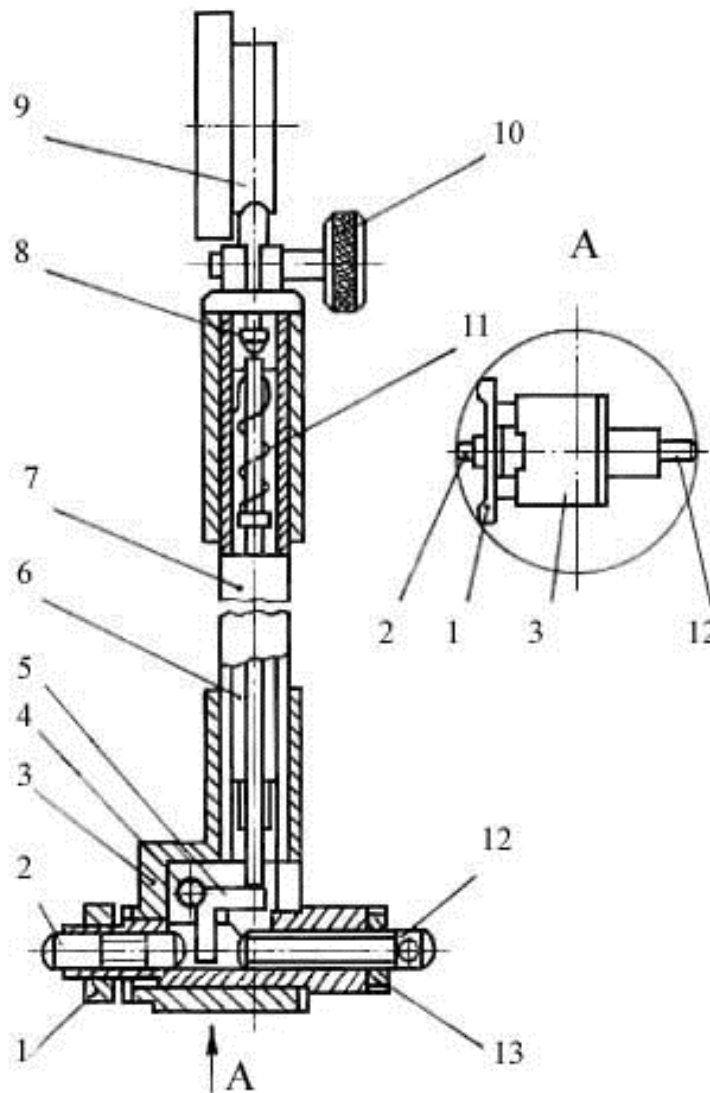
Схема индикаторного нутромера: 1 – центрирующее устройство; 2 – измерительный наконечник; 3 – корпус; 4 – ось; 5 – рычаг; 6 – шток; 7 – трубчатый корпус; 8 – измерительный стрежень индикатора; 9 – индикатор; 10 – винт; 11 – пружина; 12 – сменная измерительная вставка; 13 – контргайка
